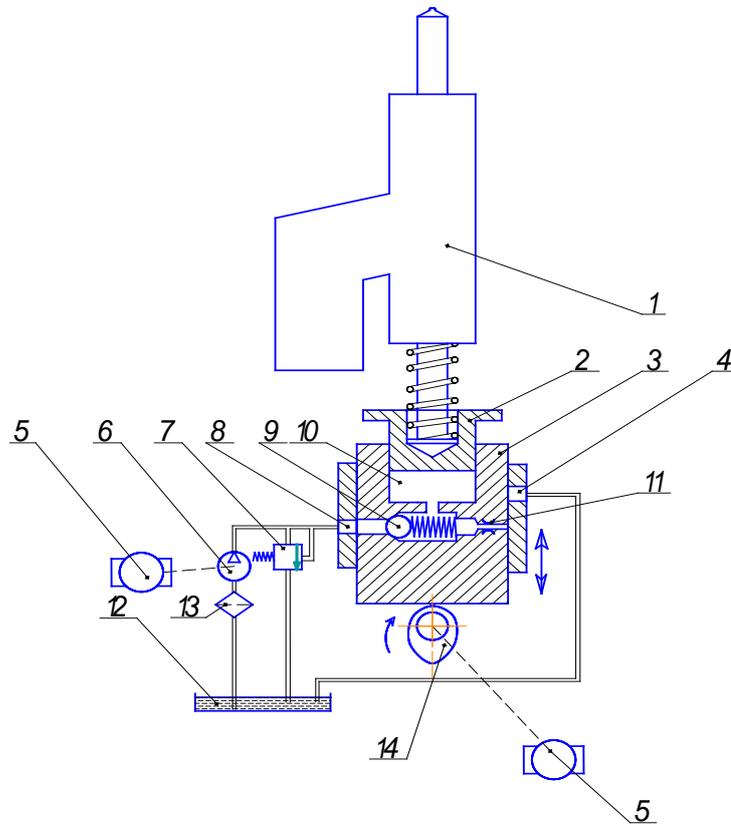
Универсальное устройство для проверки насос-форсунок
